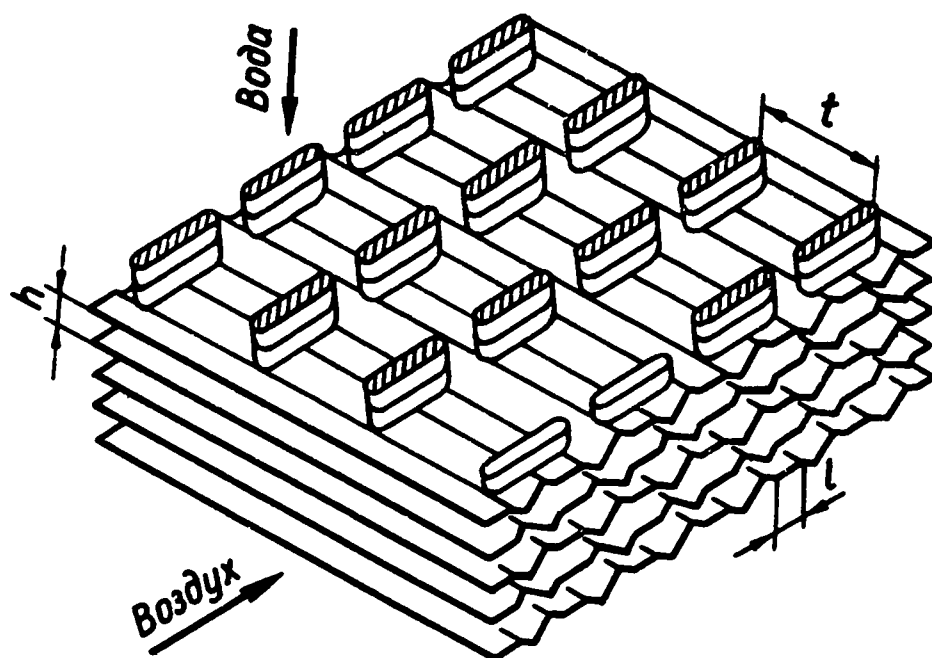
Прямоугольные каналы поверхностей с двухмерными попарно сопряженными выступами и канавками в конструкции трубчато-пластинчатого водяного радиатора
